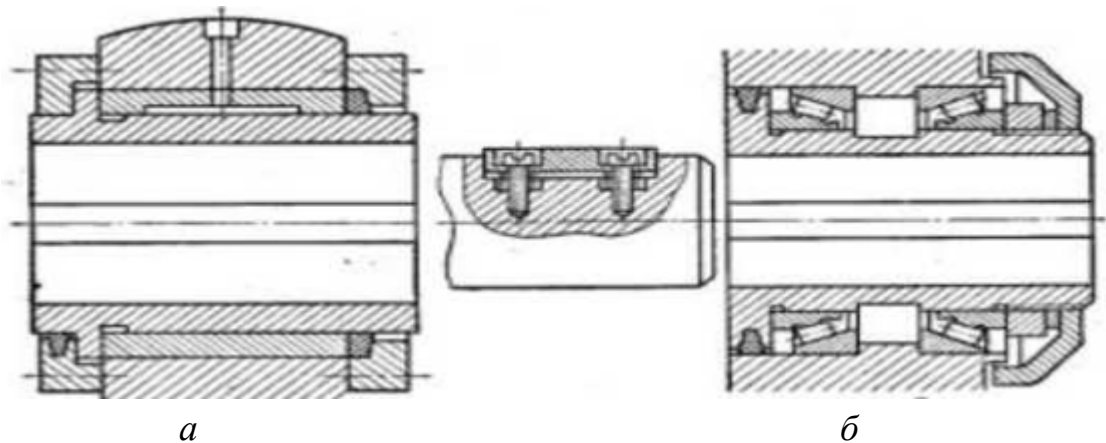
Конструкція напрямних втулок на підшипниках:
